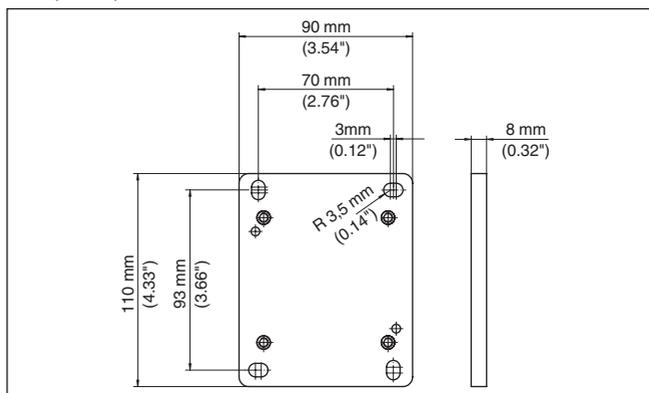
Gabarito de orifícios - Placa de montagem na parede (caixa externa)
